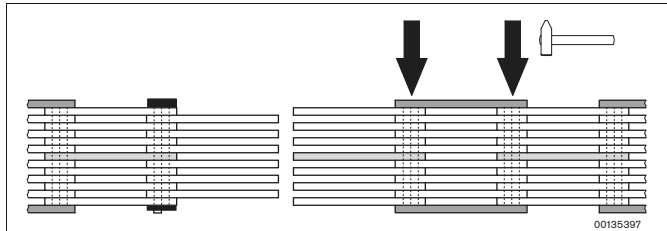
Acortar: hacer saltar la costura de soldado
